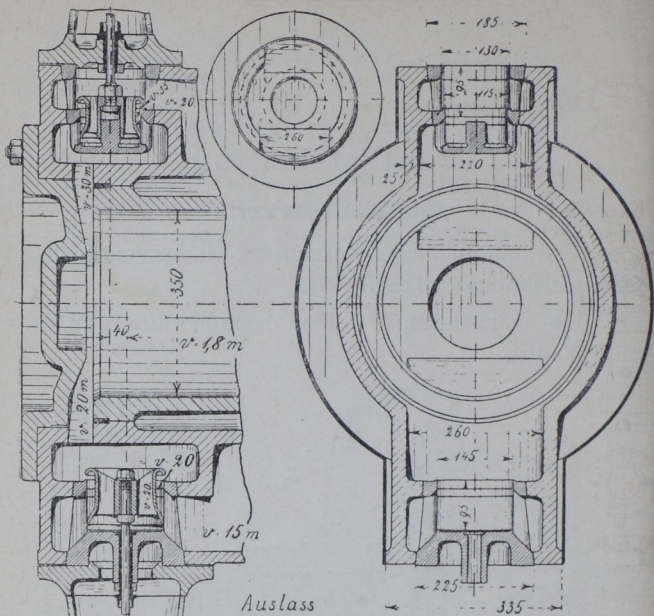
402. Ventilsteuerung für 350 mm Cylinderdurchmesser.
